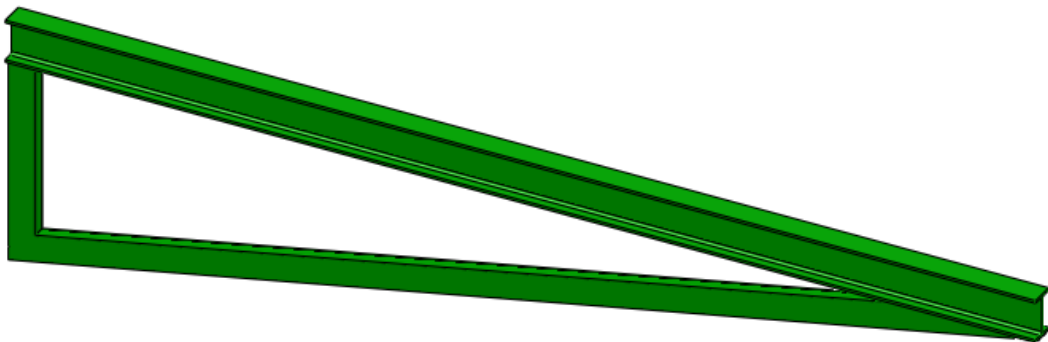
Viga reforzada de la estructura del plato giratorio.
